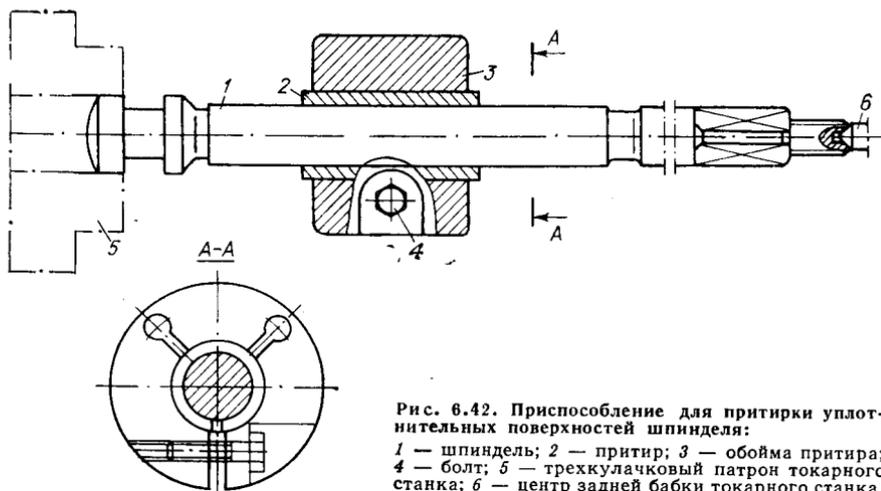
Приспособление для притирки уплотнительных поверхностей шпинделя:
